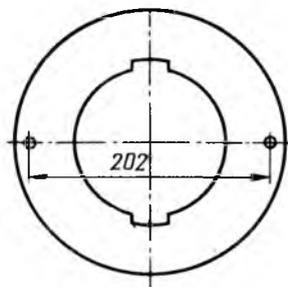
Диск для крепления ножа, устанавливающийся на место щетки
